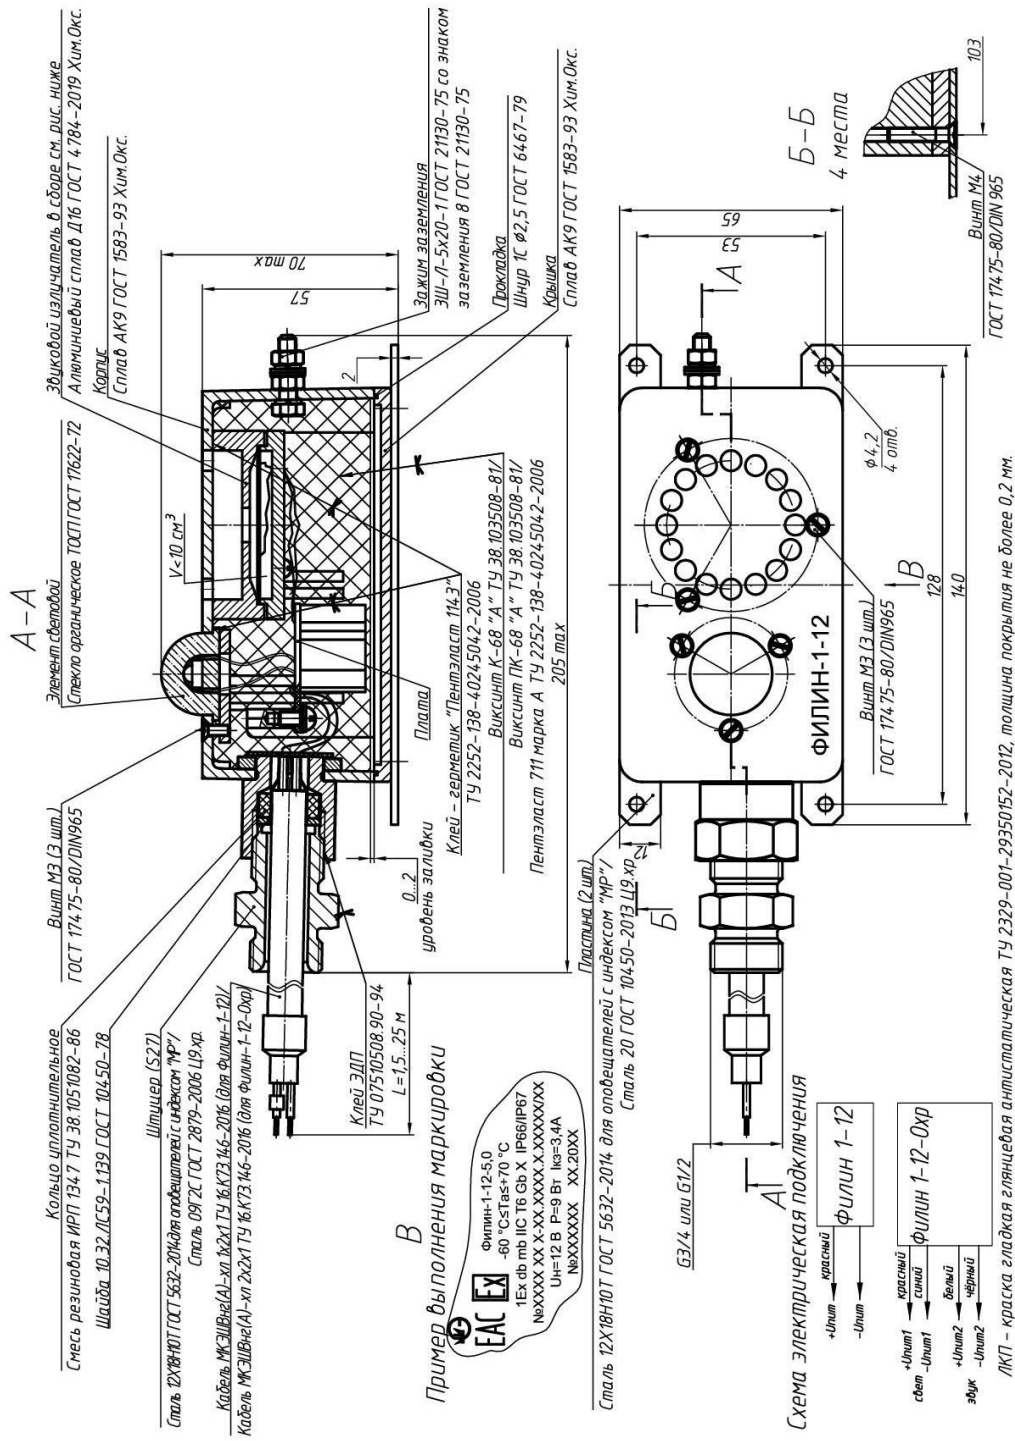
а – Габаритный чертёж оповещателей ФИЛИН-1-12, ФИЛИН-1-12-Охр, совмещённый с чертёжом средств взрывозащиты. Примеры выполнения маркировки см в п. 6.2
